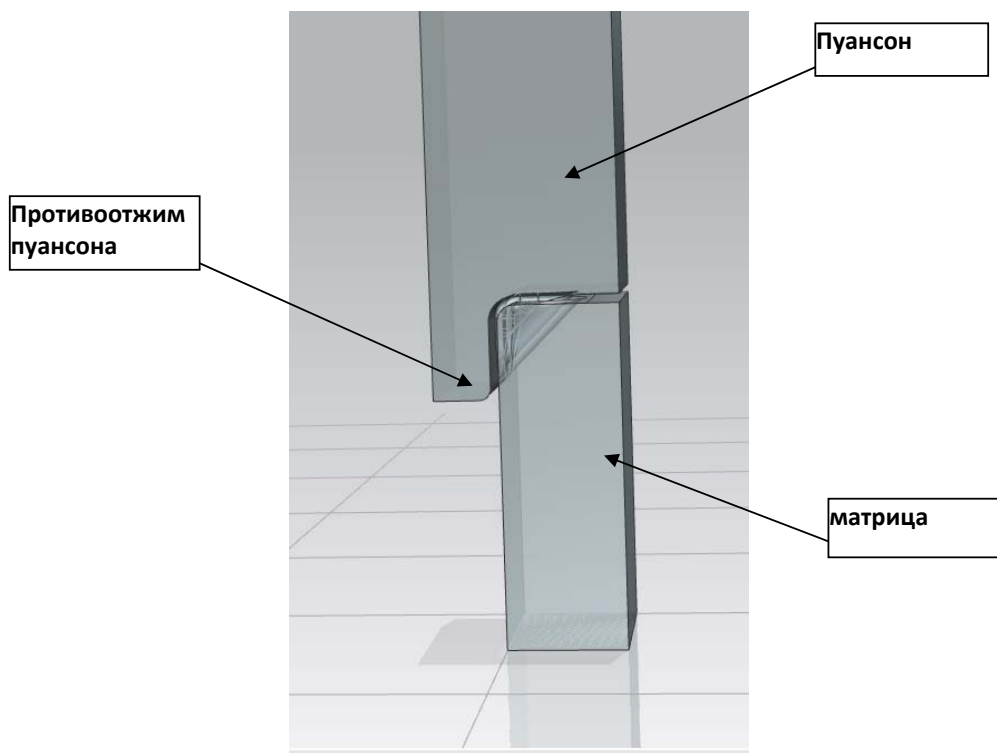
ЭМ матрицы и пуансона для операции Гибка-формовка изготовления детали «Держатель»
